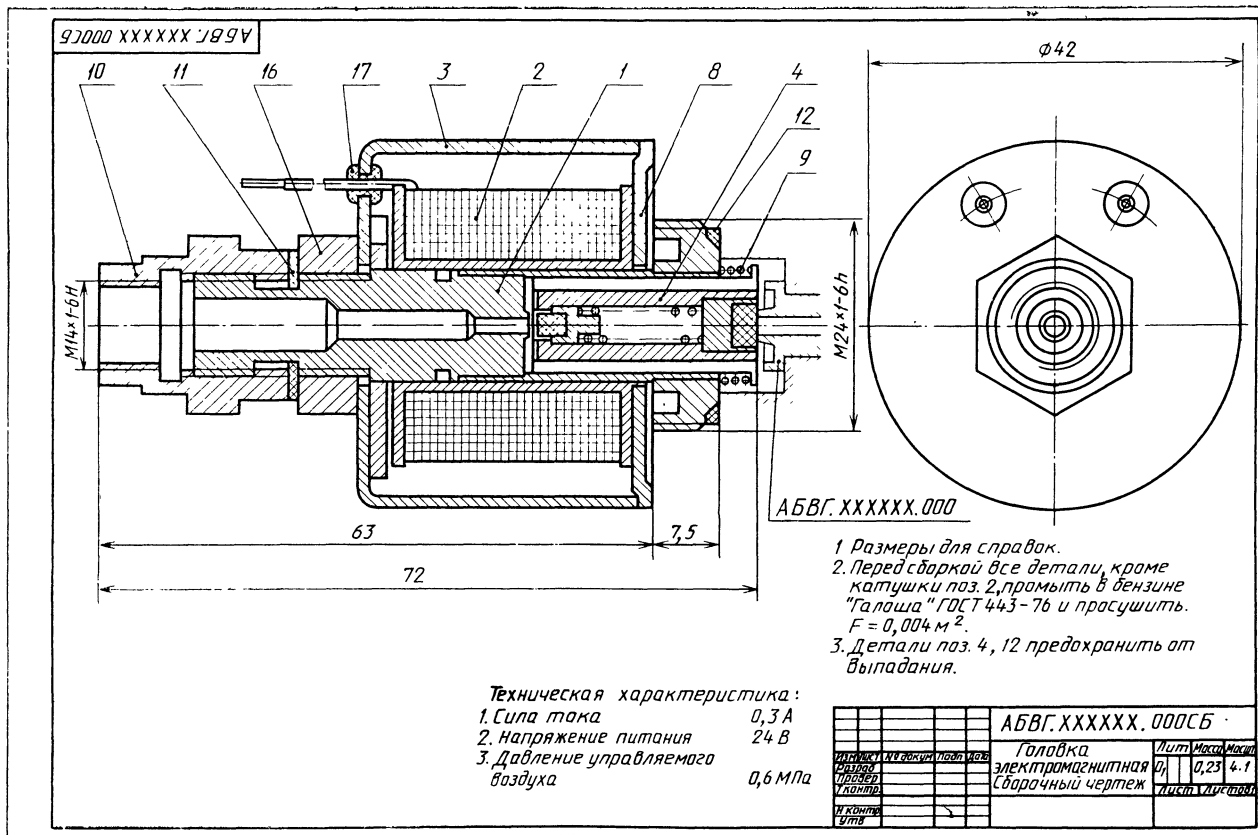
, а. Сборочный чертеж электромагнитной головки
